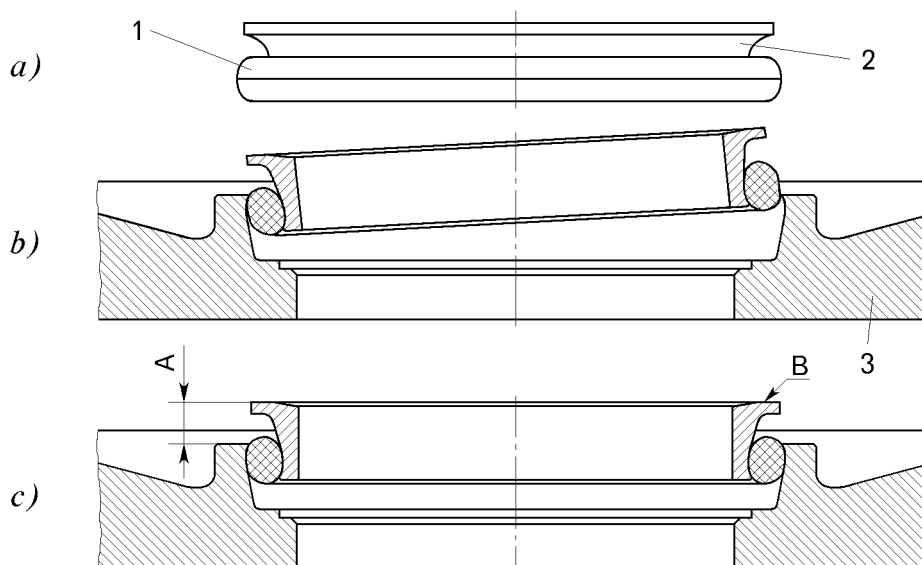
Установка торцовых резинометаллических уплотнений:
